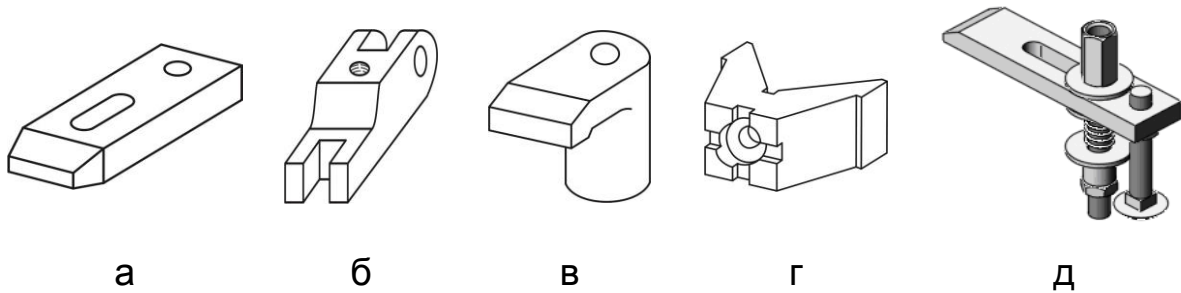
Приклади притискних деталей та пристроїв: а – планка пересувна плоска; б – планка поворотна; в – наконечник Г-подібний; г – наконечник призматичний; д – прихоплювач
